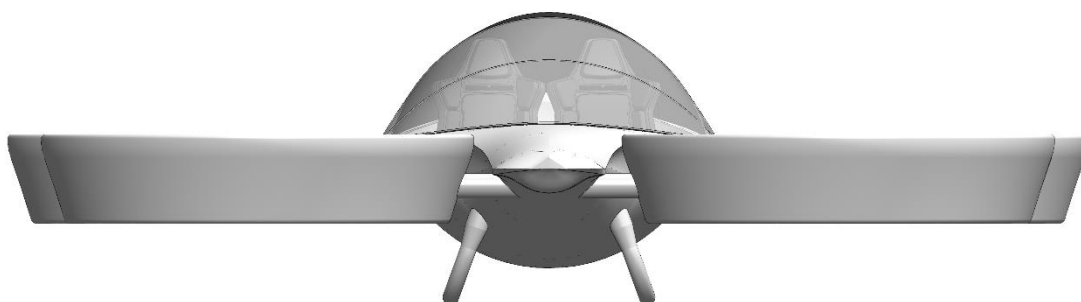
Vista frontal alzado. Fuente: elaboración propia
